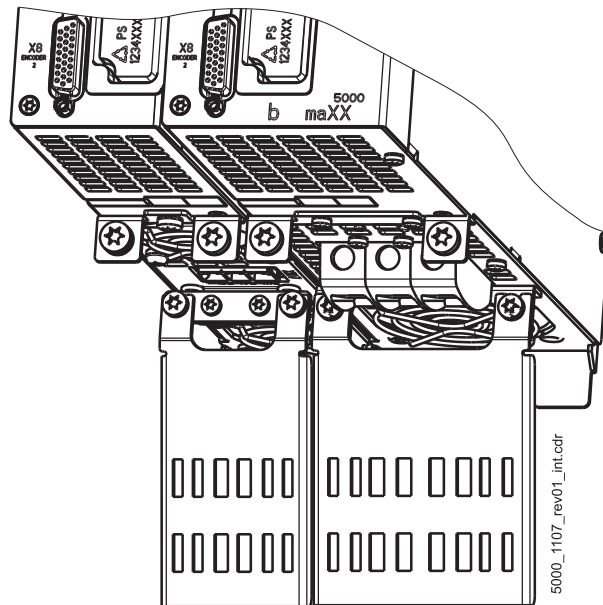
Montage Schirmblech luftgekühlte Geräte
